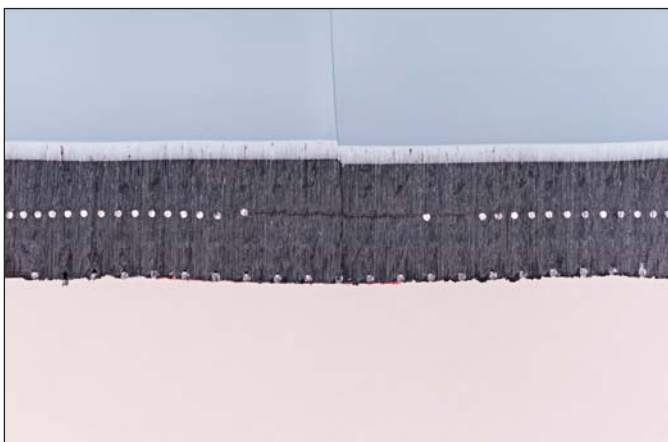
Schnittbild durch eine Heizwendelschweißung
